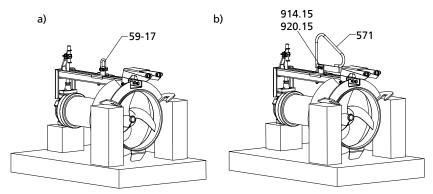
Amaline con: a) Grillete 59-17 b) Estribo 571
